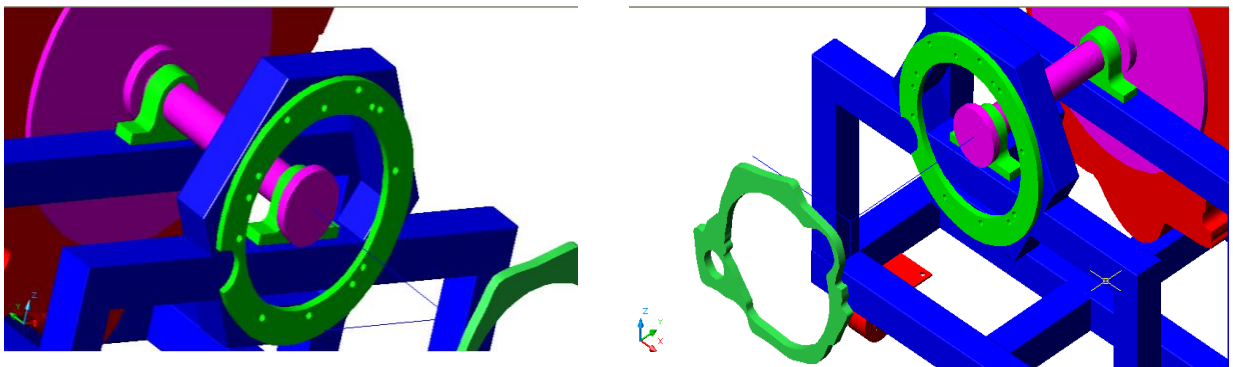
Detalles tridimensional de la sección de sujeción de las cajas en el Banco.
